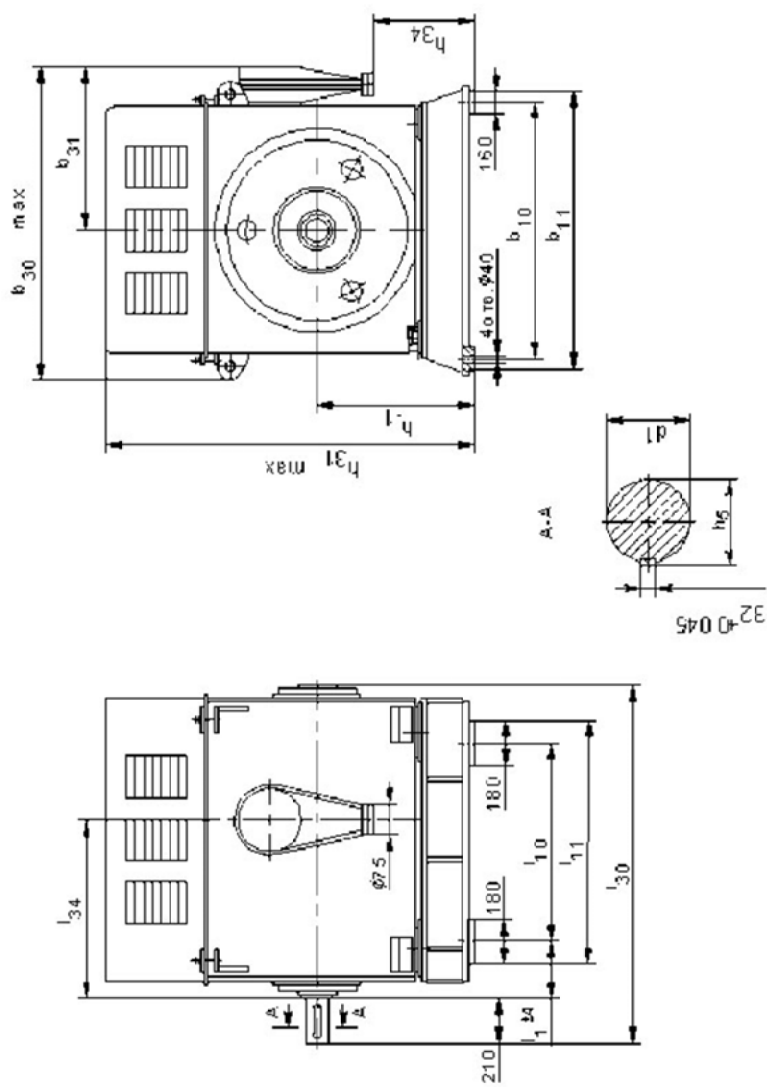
Габаритные, установочные, присоединительные размеры двигателей серии А4 12 и 13 габарита
